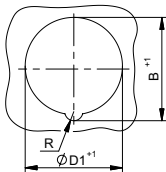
Розетки встраиваемые / Figure 5 – Built-in socket-outlets / 5 сурет – Кіріктірілетін розеткалар
